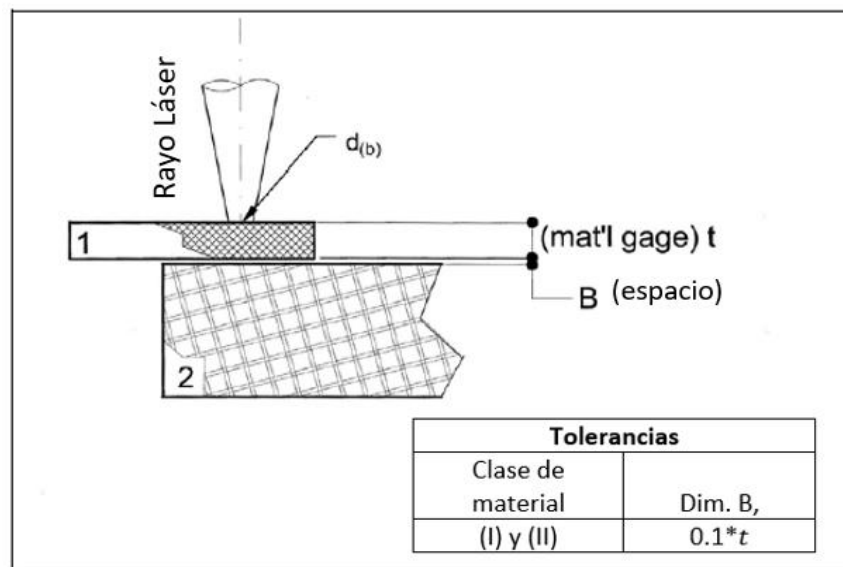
Junta de soldadura de solape para soldadura láser: tolerancias sugeridas para el espacio. El gap(B) no es una función del diámetro del rayo láser. La disposición preferente es que la pieza de calibre más delgada (1) esté encima de la pieza de calibre más pesada (2). Las abrazaderas deben presionar las dos piezas juntas durante la configuración y durante el proceso de soldadura.[3]
